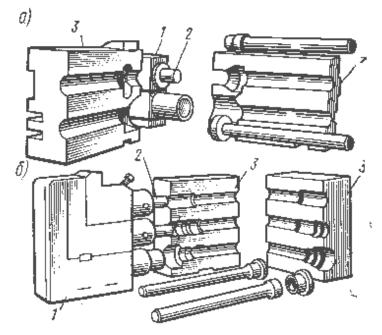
Схемы штампов горизонтальноковочных машин: а – двухручьевой; б – трехручьевой; 1 – блок пуансонов; 2 – пуансон; 3 – полуматрицы
